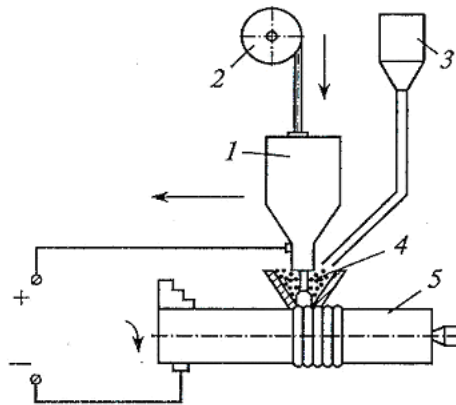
Схема автоматической дуговой наплавки цилиндрических деталей под флюсом: 1 – патрон; 2 – кассета; 3 – бункер; 4 – флюс; 5 – деталь
